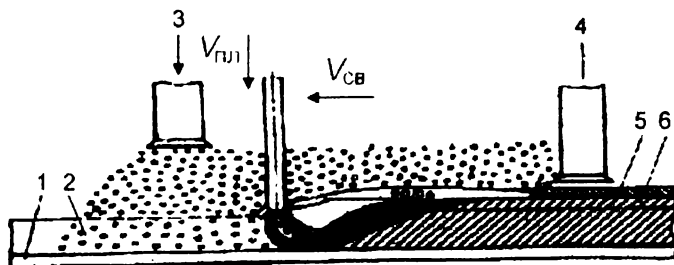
Схема процесса автоматической сварки под флюсом:
